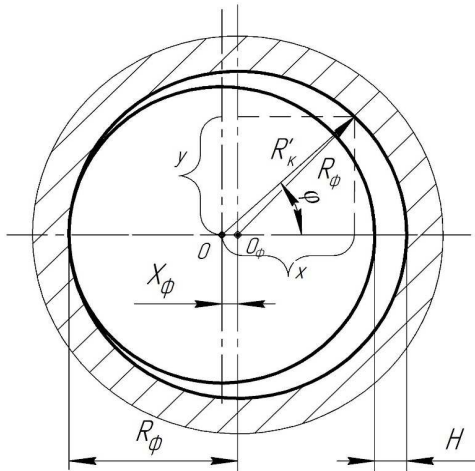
Схематический профиль резьбы в полярной системе координат
